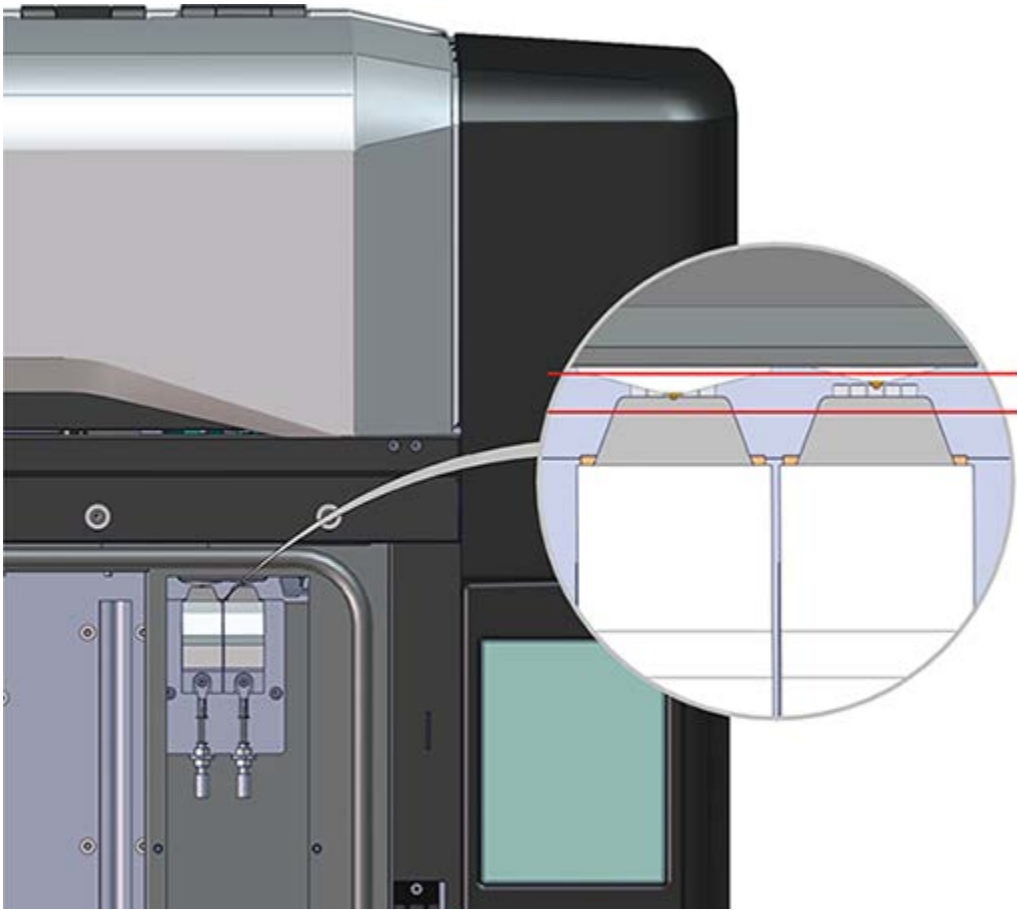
Emplacement des molettes de réglage en hauteur du nettoyage d'embout
